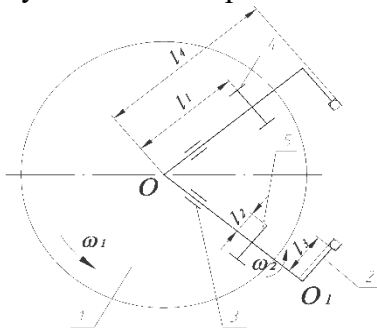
Розрахункова схема черпакового механізму точного висіву дрібнозернинного насіння
